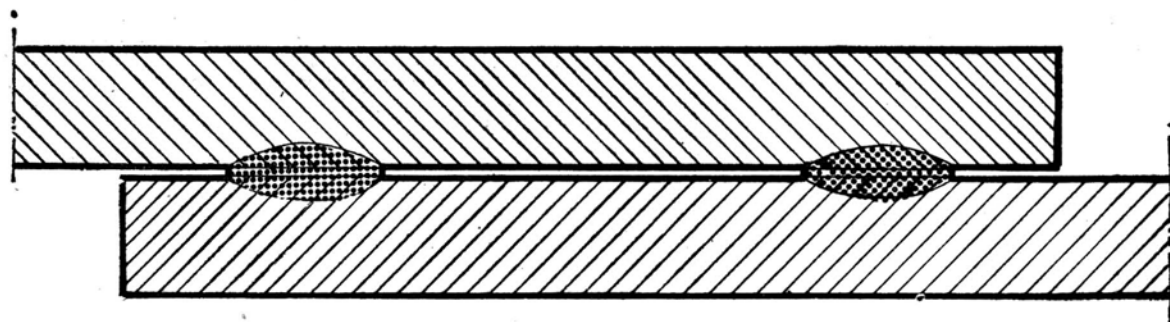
SOLDADURA POR PUNTOS (PROCEDIMIENTO IV)
